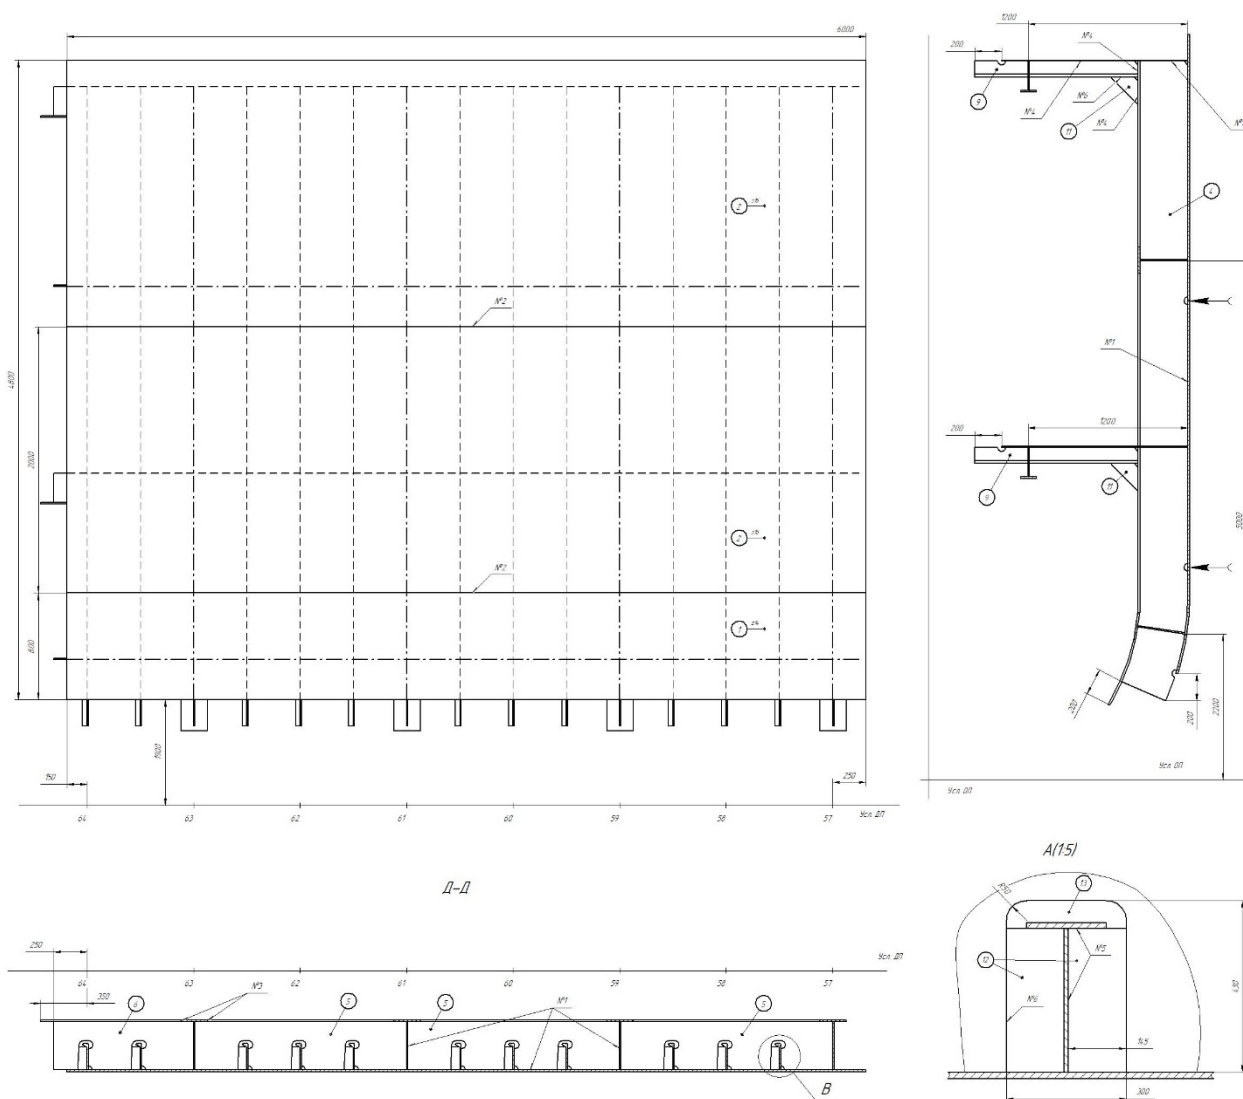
Выполнение сварных швов при изготовлении бортовой секции
